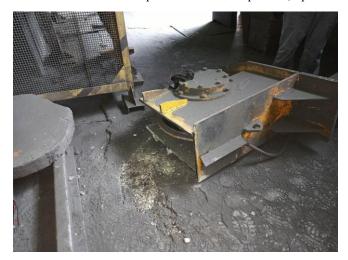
Полное разрушение сварных соединений по границе металла сплавления стенок модуля холостого колеса с вертикальным листом концевой балки со стороны кабины крановщика
